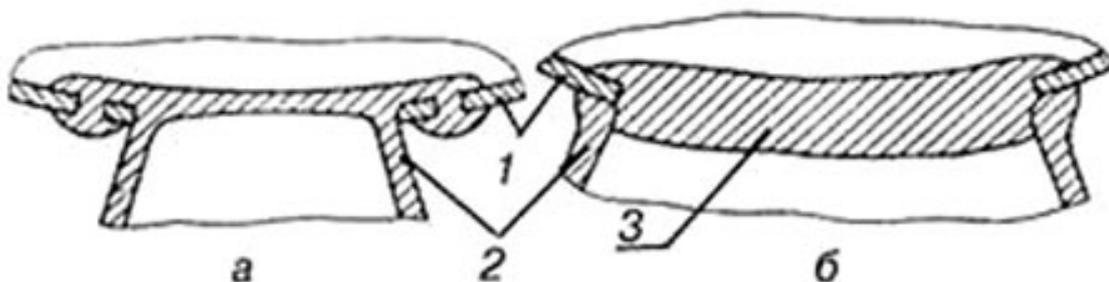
Типы стыка корпуса и ножки составных бронзовых котлов из скифских курганов: а – Келермес [94], б – Солоха. [72]
